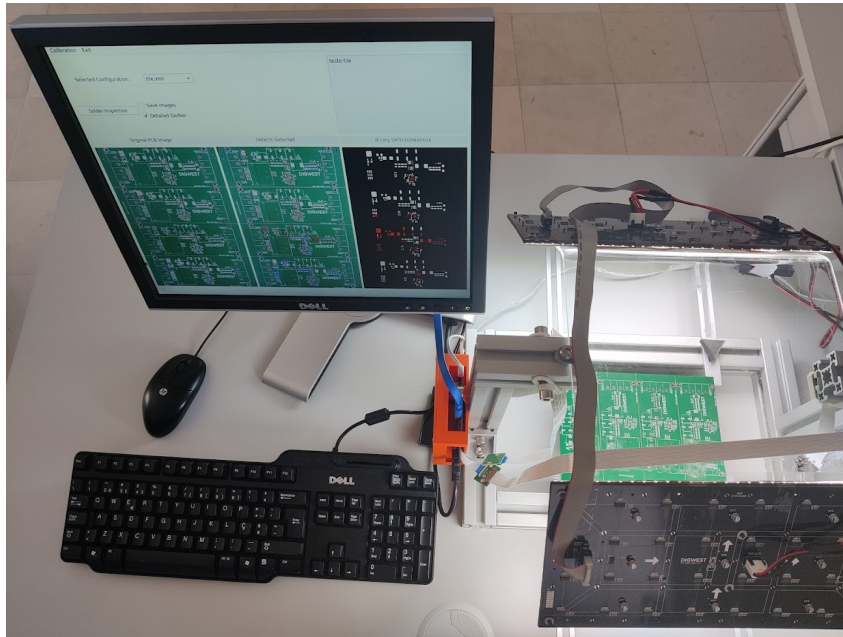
Versão final do protótipo do sistema de inspeção.
